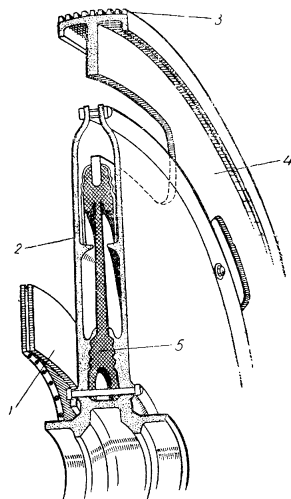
Конструкция колеса рекордного автомобиля Л. Шмидта: 1 — дисковый тормоз; 2 — внутренний диск колеса; 3 — кольца из рояльной проволоки; 4 — внешний диск колеса; 5 — резиновый диск
